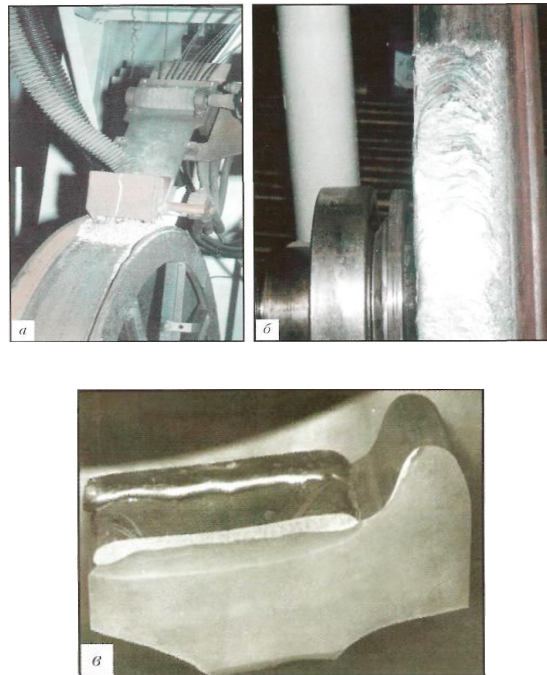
Установа УНО-2 для наплавлення обода колеса десятима електродами в одній зварювальній ванні дротом Св-08ХМ діаметром 3 мм під флюсом АН-60: *а* – зварювальна головка; *б* – колесо з наплавленим ободом [11]
